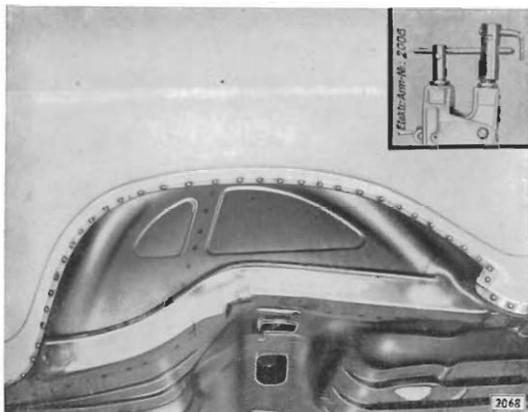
Seitenwand am hinteren Radeinbau punktgeschweißt
